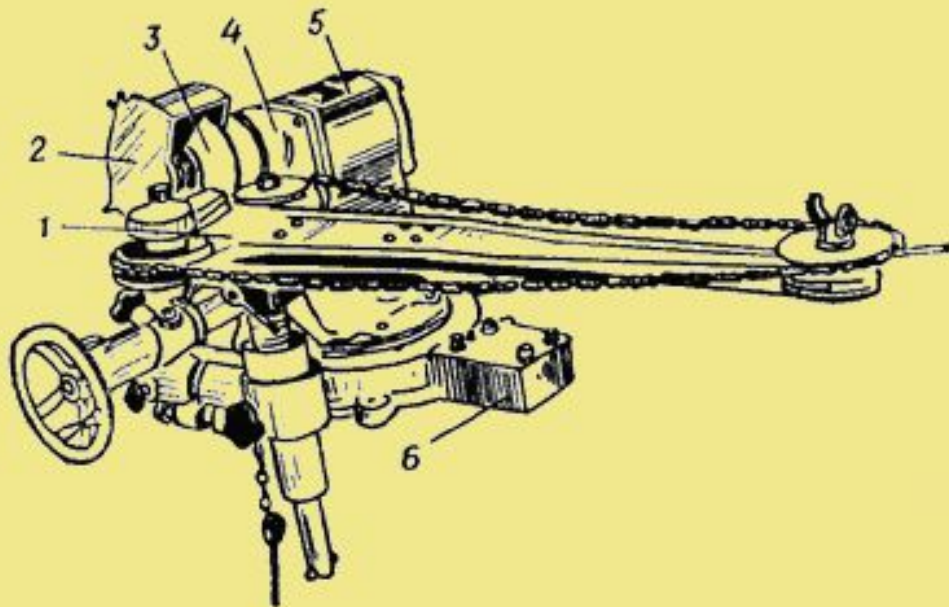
Настольный заточной станок ИЭ 9704 (И155)
